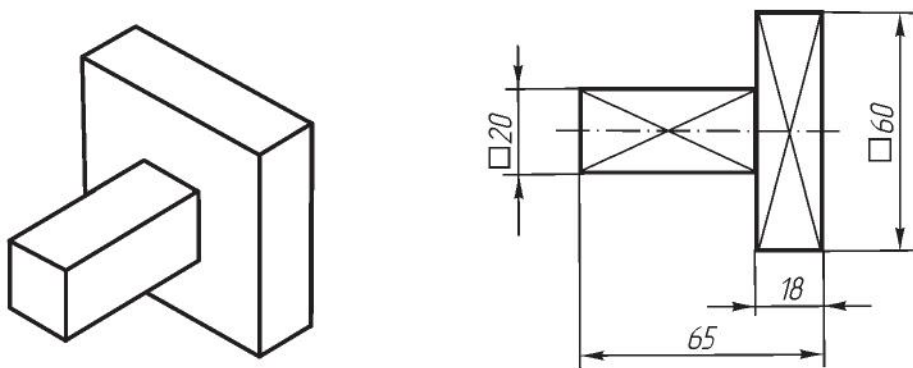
Обозначение на чертеже плоской поверхности
